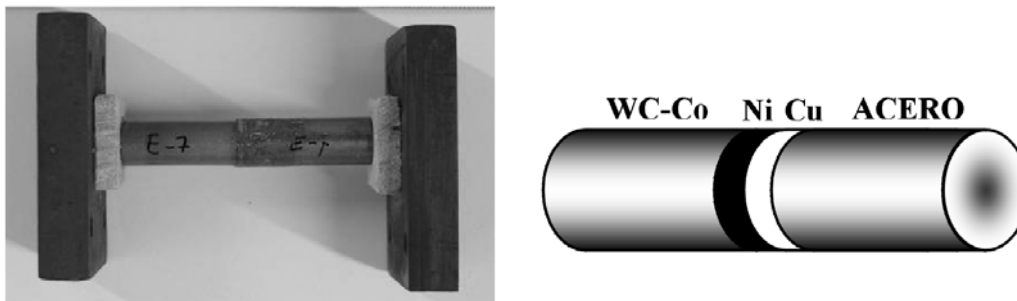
Disposición de las probetas para el ensayo de soldadura por difusión a vacío
